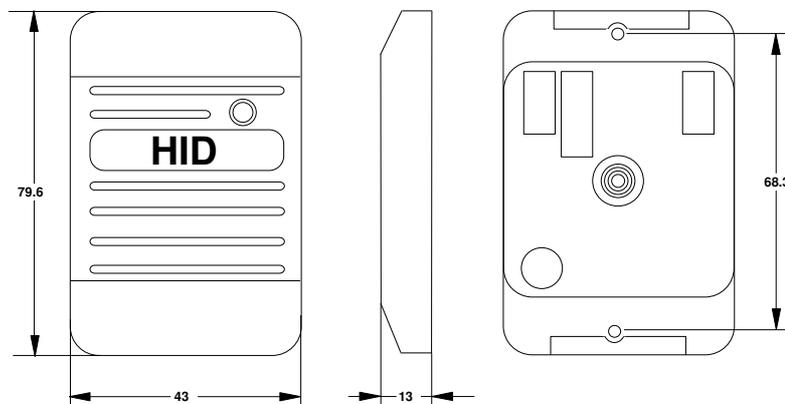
Внешний вид и габаритные размеры (в мм) считывателя ProxPoint
